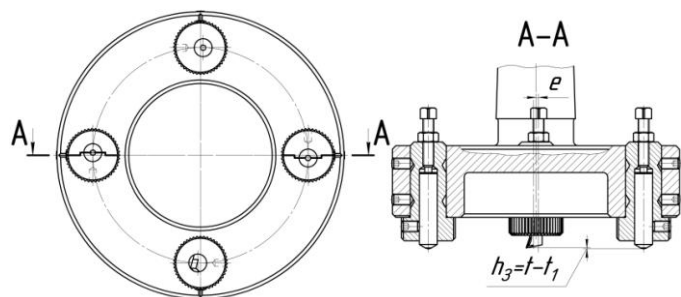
Комбинированный инструмент для обработки ПТП ЭДМ
